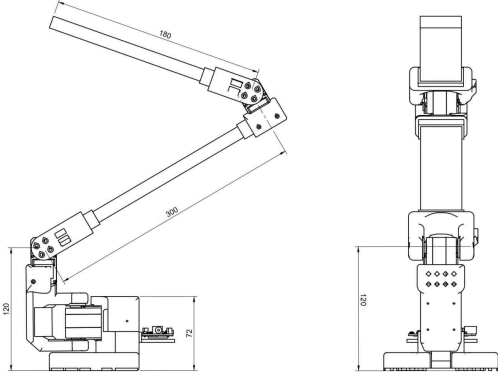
실험 장비의 CAD 도면 및 주요 치수
